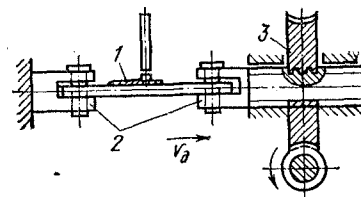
Схема машины для определения сопротивляемости металла сварного шва образцов при сварке:
